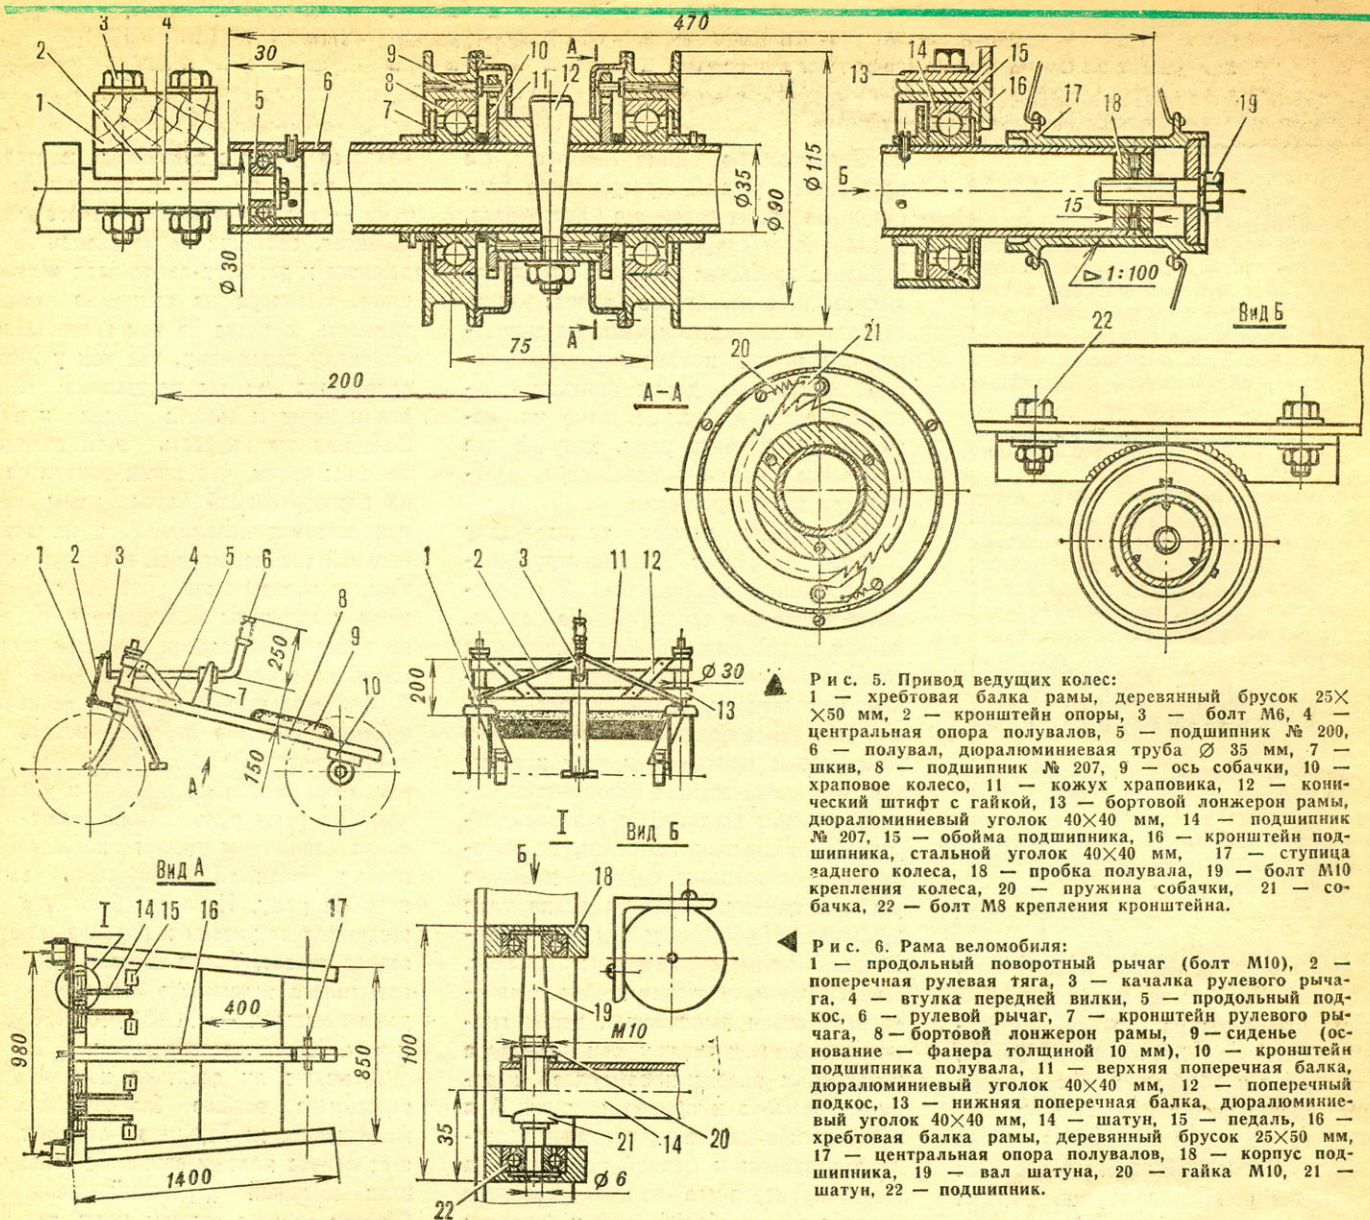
Привод ведущих колес: 1 — хребтовая балка рамы, деревянный брусок 25×50 мм, 2 — кронштейн опоры, 3 — болт М6, 4 — центральная опора полувалов, 5 — подшипник № 200, 6 — полувал, дюралюминиевая труба  $\varnothing$  35 мм, 7 — шкив, 8 — подшипник № 207, 9 — ось собачки, 10 — храповое колесо, 11 — кожух храповика, 12 — конический штифт с гайкой, 13 — бортовой лонжерон рамы, дюралюминиевый уголок 40×40 мм, 14 — подшипник № 207, 15 — обойма подшипника, 16 — кронштейн подшипника, стальной уголок 40×40 мм, 17 — ступица заднего колеса, 18 — пробка полувала, 19 — болт М10 крепления колеса, 20 — пружина собачки, 21 — собачка, 22 — болт М8 крепления кронштейна.
